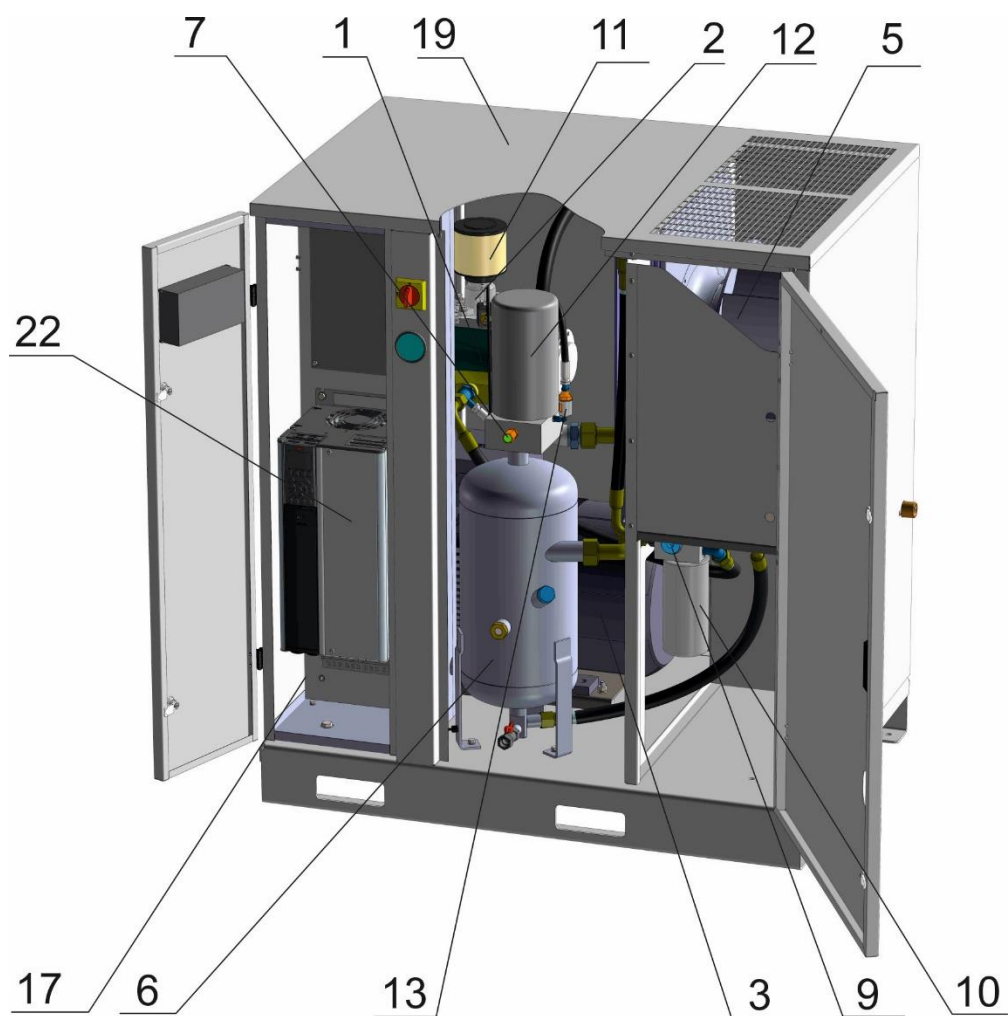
Общий вид компрессорной установки ВК25-...(ВС), ВК30-...(ВС)
